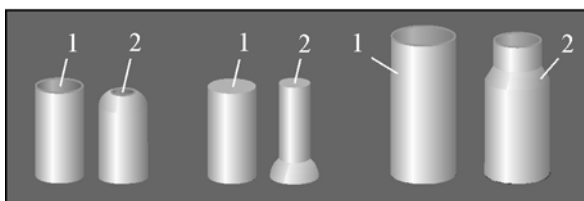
Заготовки 1 та деталі 2, що отримані обтискуванням
